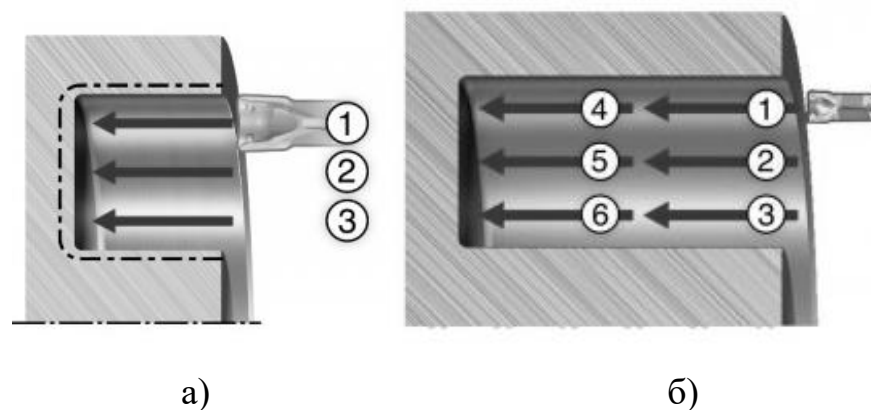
Схеми обробки торцевих канавок різної глибини
